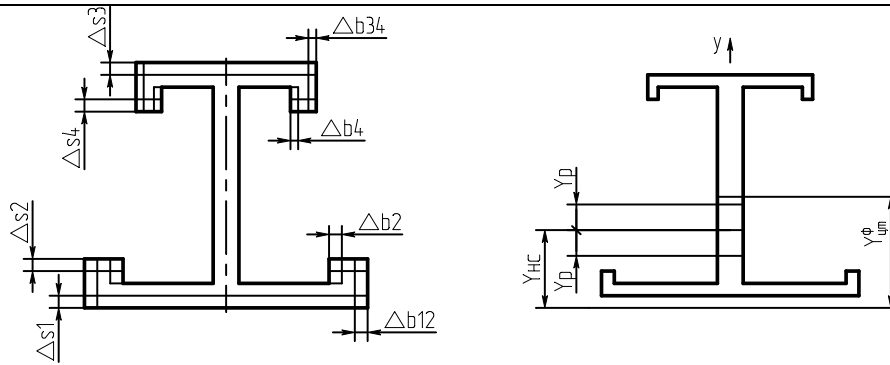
Схема поперечного сечения заготовки после фрезерования
